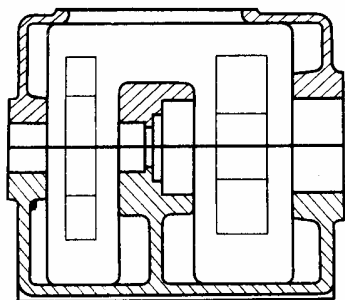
Корпус с разъемом в плоскости осей валов соосного редуктора
